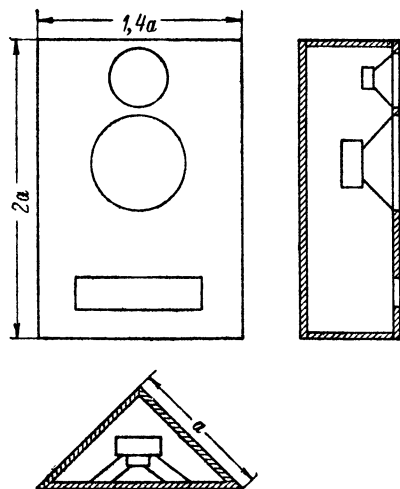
Конструкция и размеры призматического фазоинвертора.
